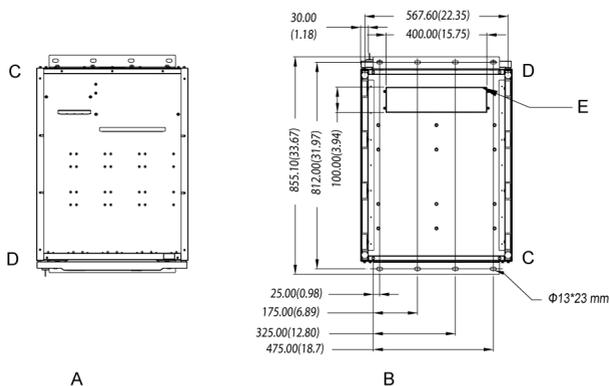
Габаритные размеры шкафа ИБП на 100–120 кВА (вид сверху и снизу)
